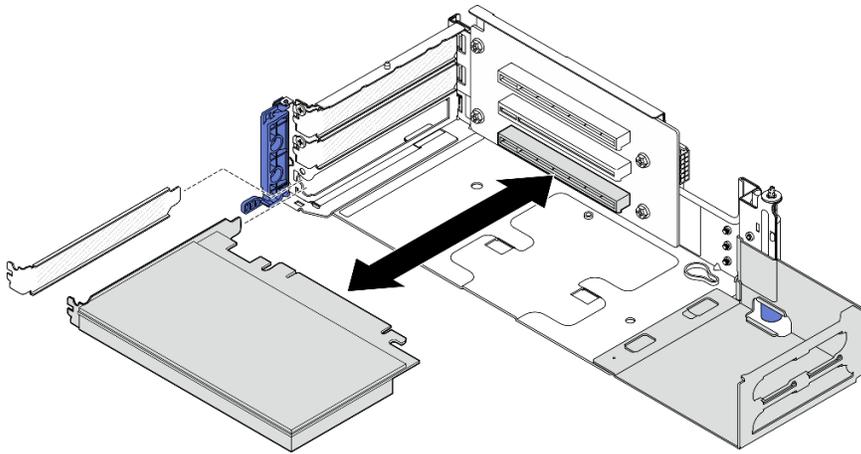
Instalación de un adaptador PCIe en la tarjeta de expansión PCIe 2
